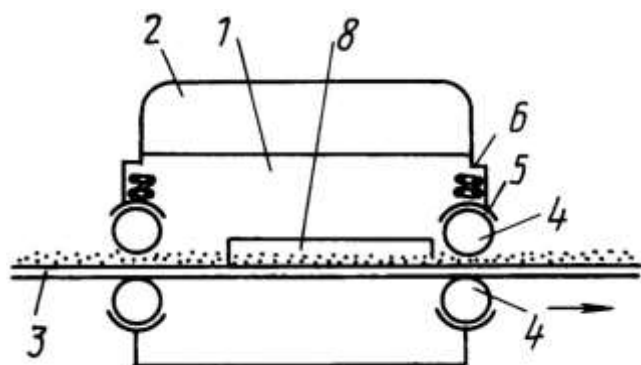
Сушилка непрерывного действия в разрезе, вид сбоку
